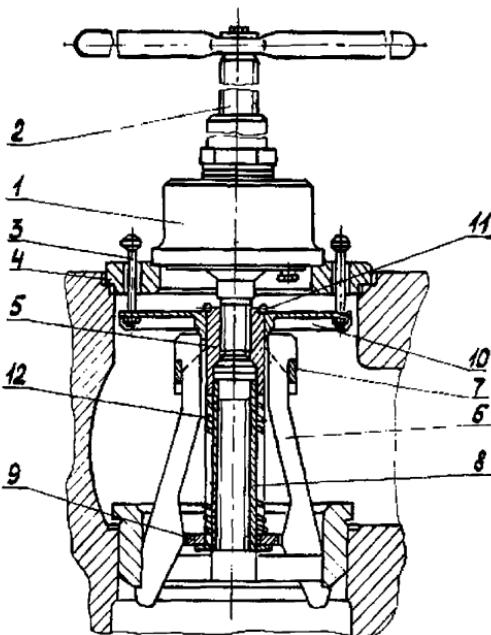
Приспособление для демонтажа седел клапанов гидравлической части паровых насосов НПН-3 и ИНПНС (тип II):
